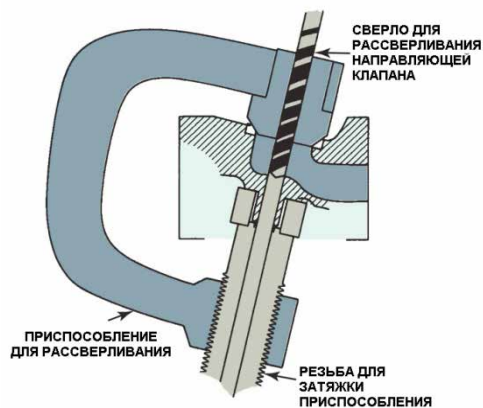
Типовое приспособление, используемое для расточки направляющей для принятия тонкостенного вкладыша; источник: Pearson Education, Inc.
